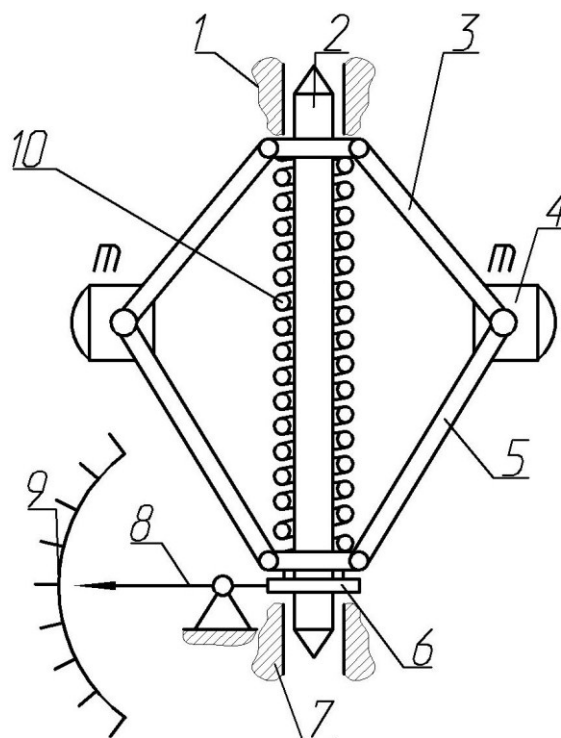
Кинематическая схема механического центробежного тахометра: 1 — подшипник; 2 — вал; 3 — рычаг; 4 — груз; 5 — рычаг — пружина; 6 — скользящая муфта; 7 подшипник; 8 — стрелка; 9 - шкала.
